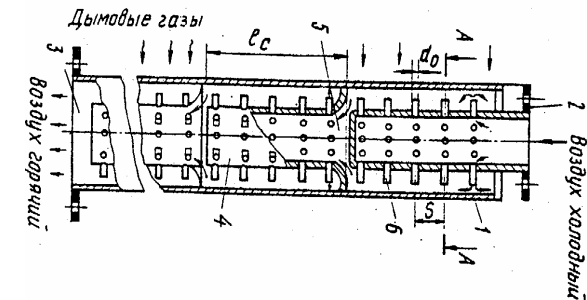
Струйный рекуператор [26]: 1) корпус; 2) патрубок подачи холодного воздуха; 3) выходной патрубок нагретого воздуха; 4) поля вставки; 5) входной проем; б) газовыпускное отверстие с патрубком
